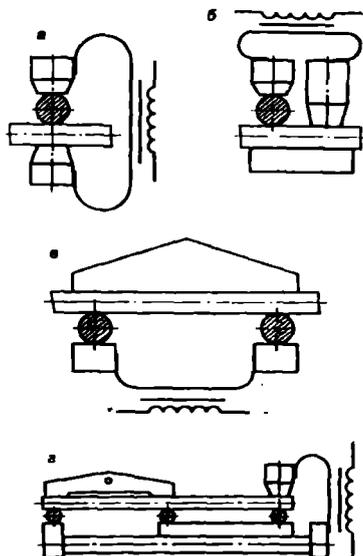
Схемы подвода сварочного тока:
